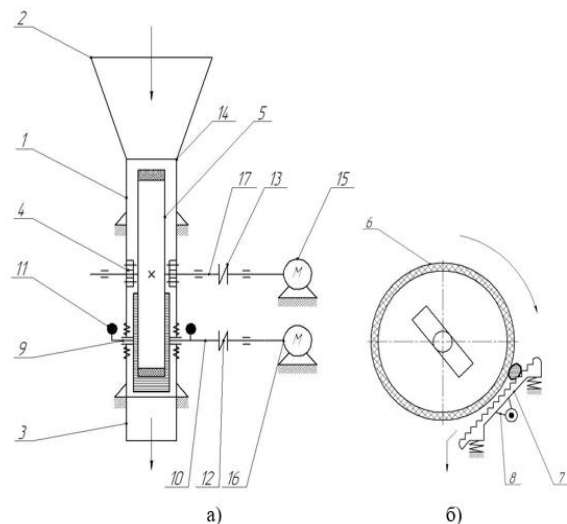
, а) – принципова схема вібраційного обладнання для луцення волоського горіха з окремим дебалансним віброприводом, б) – робочі органи обладнання: 1 – корпус; 2 – завантажувальний бункер; 3 – розвантажувальна горловина; 4 – варіативний механізм; 5 – дробильне колесо; 6 – гумове покриття; 7 – підпружинене рифлене деко; 8 – опори; 9 – підшипникові вузли; 10 – приводний вал; 11 – дебаланси; 12, 13 – еластичні муфти; 14 – шиберна заслінка, 15, 16 – електродвигуни; 17 – приводний вал дробильного колеса
